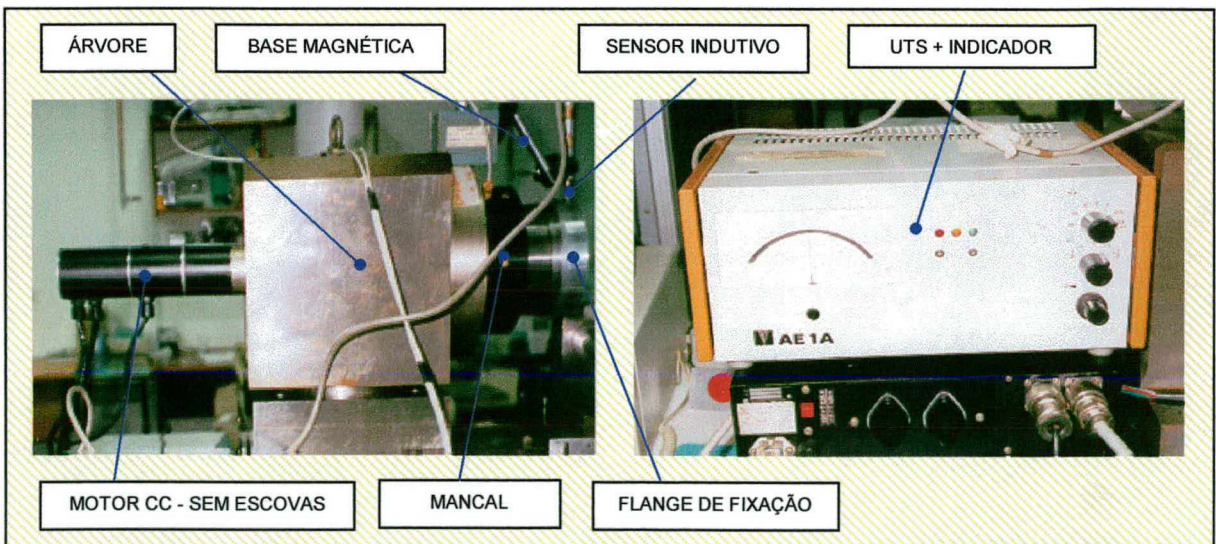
Equipamento utilizado na centragem da flange de montagem.
